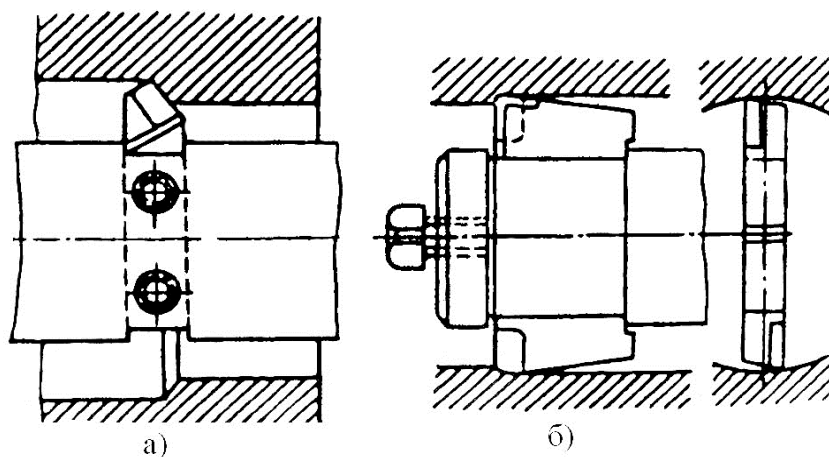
Схеми закріплення різця (а) і розточувальної пластини (б) в борштанзі
